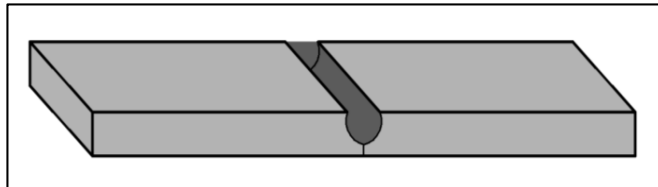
Soldadura de Penetración Parcial.
